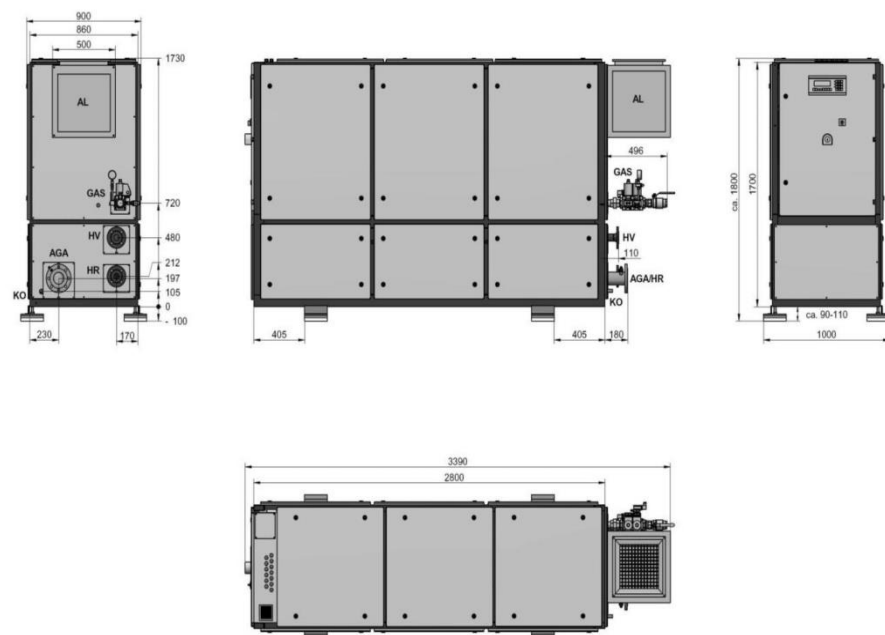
Dimensiones y empalmes del módulo de cogeneración Vitobloc 200 EM-50/81 (medidas en mm); La caja de ventilador ya montada en la parte posterior se puede desmontar para el transporte interno del módulo.
